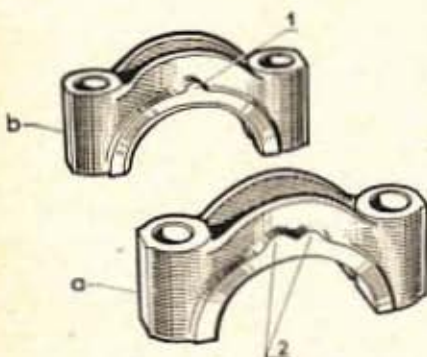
Vue des bossages d'identification des chapeaux AV (1) et milieu (2)
